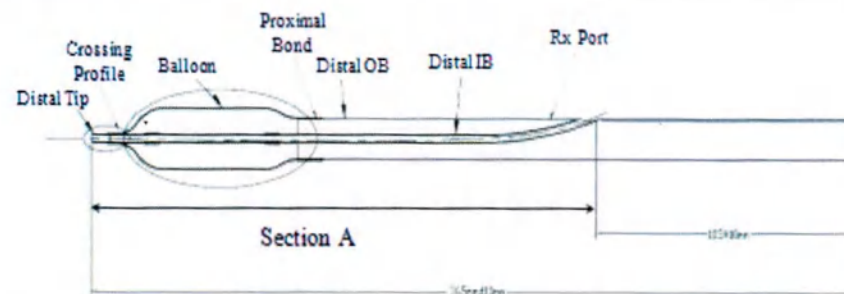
Дистальный сборочный узел/ Fig.11-5 Distal subassembly
